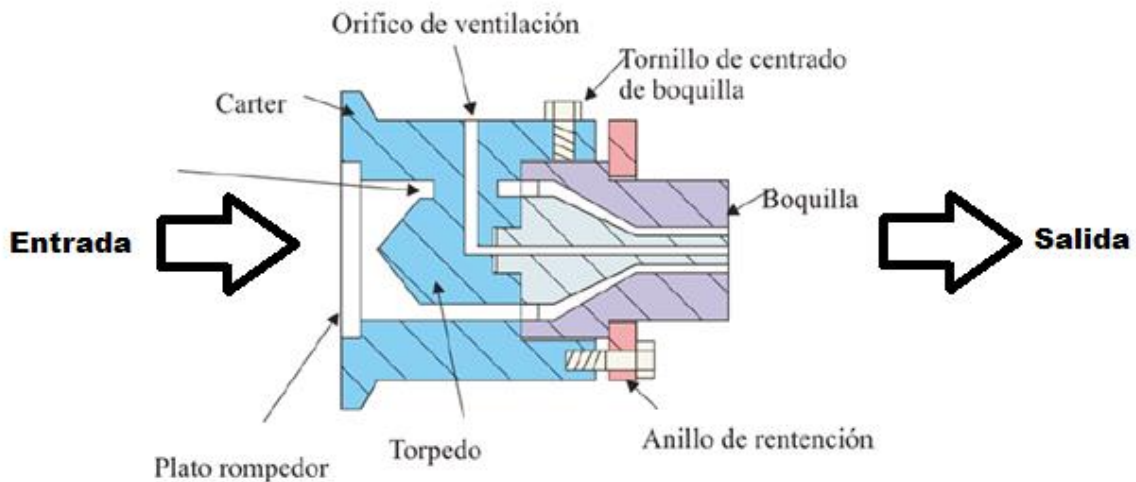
Vista lateral de una boquilla de una máquina de extrusión [18].
